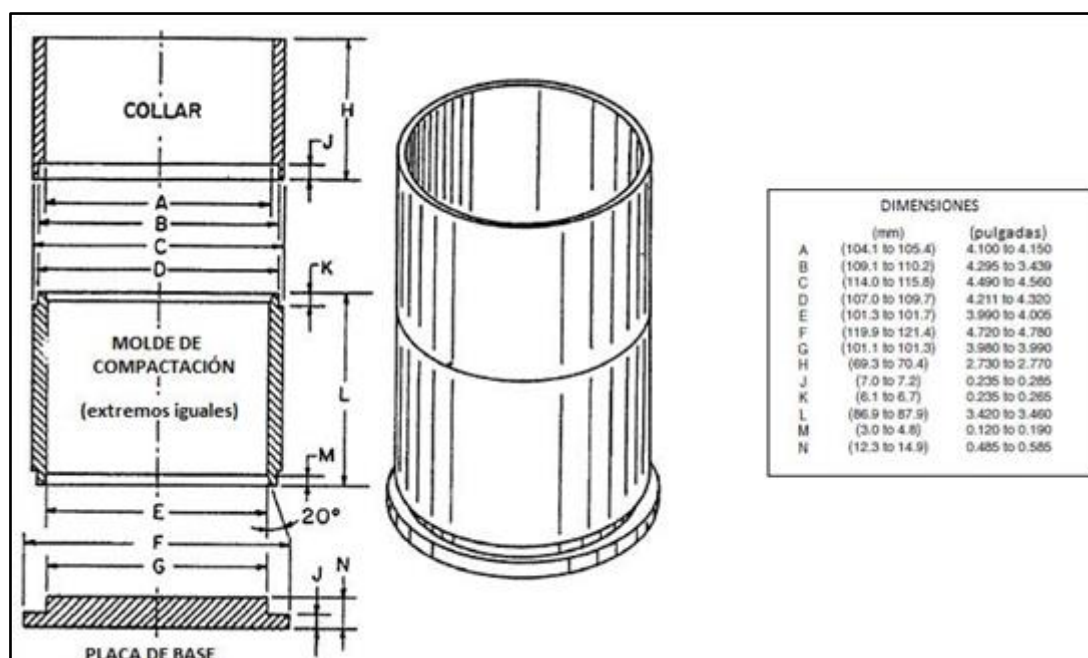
Molde para probeta Marshall. Fuente INVIAS E-748-13
